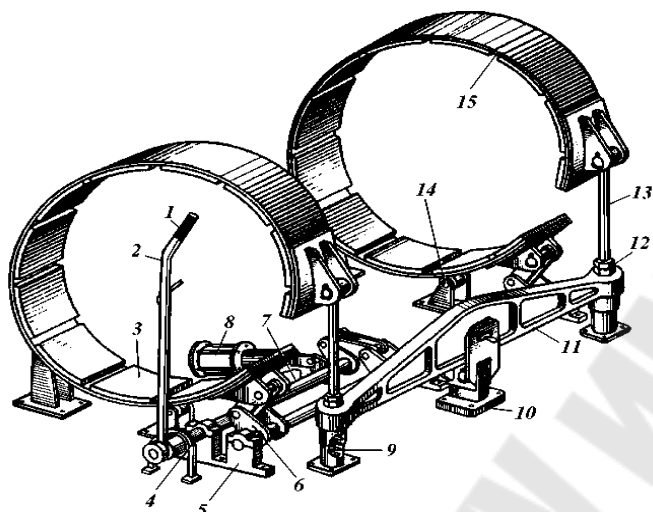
Типовой ленточный тормоз: 1 - рукоятка тормоза; 2 - рычаг; 3 - тормозная колодка; 4 - фиксатор рычага; 5 - опора кривошипного вала тормоза; 6 - рычаги; 7 - кривошипный вал; 8 - пневмоцилиндр; 9 - пружинный шарнир крепления ленты; 10 - опора балансира; 11 - балансир; 12 - контргайка; 13 - тяга; 14 - поддерживающий ролик; 15 - тормозная лента
